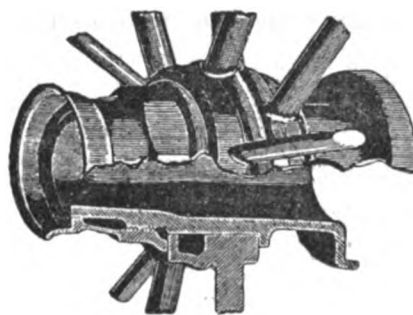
Vue d'un moyeu obtenu à la presse électrique à souder.
